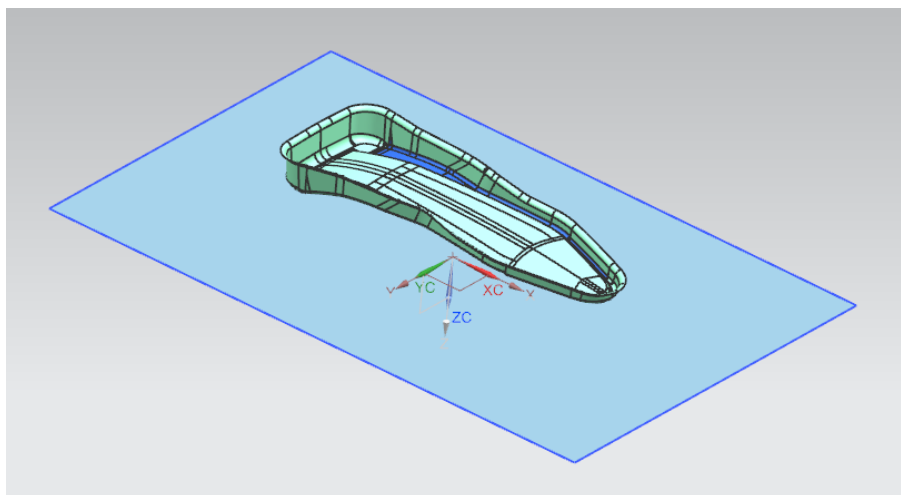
Модель для нахождения формы и размеров исходной заготовки и плоскость для развертки.
